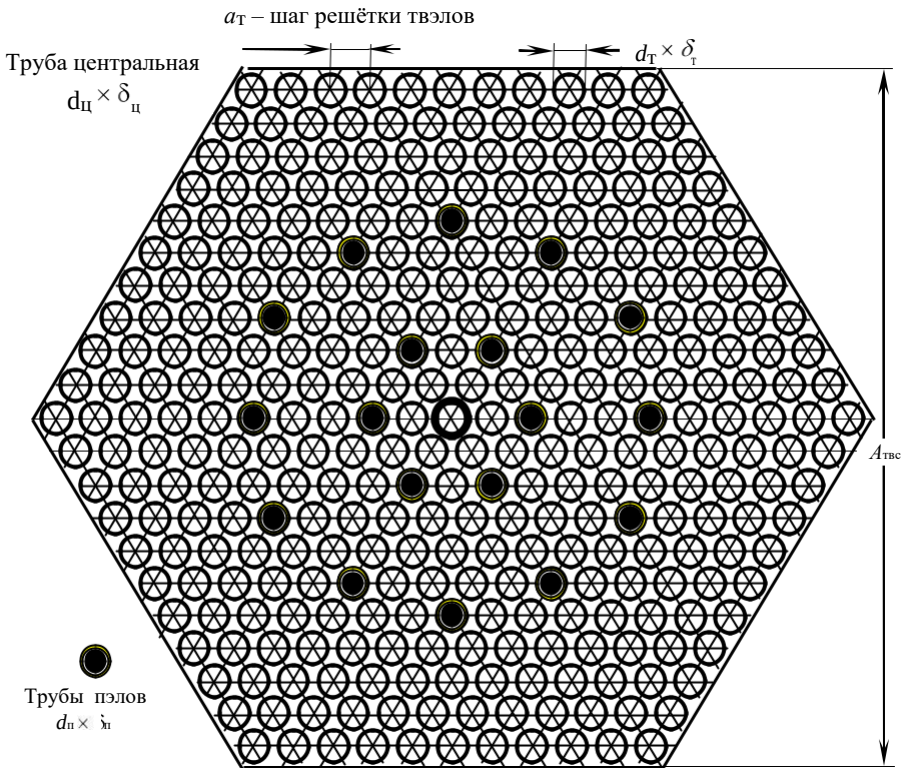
Поперечное сечение тепловыделяющей сборки
